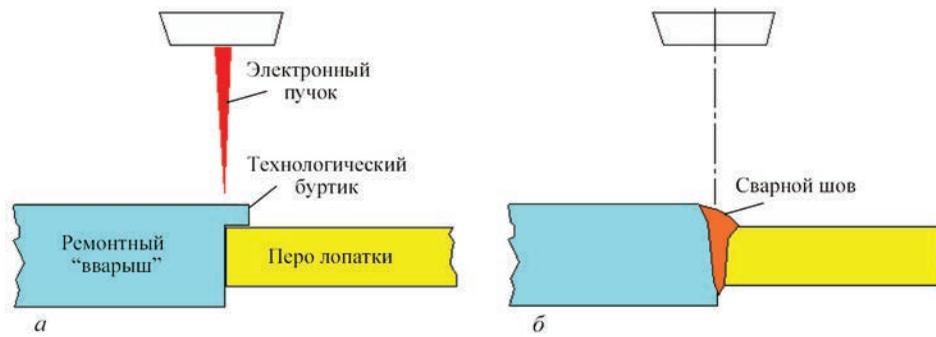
Схема ремонтного ЭЛС-соединения «вварыша» и пера лопатки: а — до сварки; б — после
